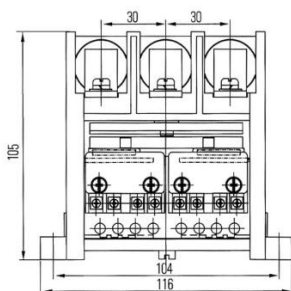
Габаритные размеры КВТ-1,14-80/125/160
